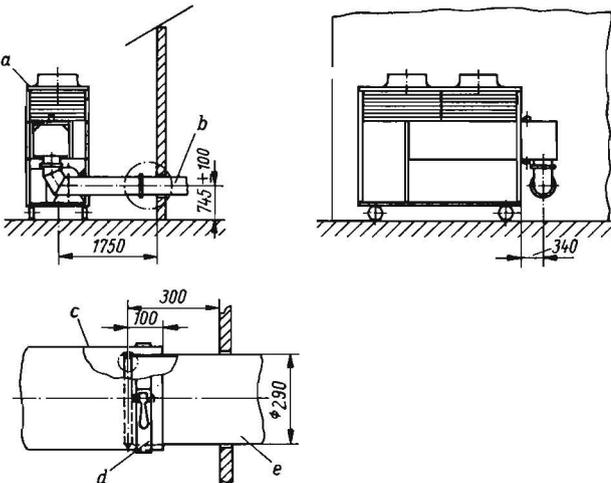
Anschluß des Getreidekühlers an ein Silo: a Maliplastik-Rohr, b Schlauchverschluß, c Stahlrohr (bauseitig), d Luftführungsröhre (Ausführung der dachförmigen Luftführungsröhre nach Angaben der zentralen Untersuchungsstelle für Getreidelagerung und Getreideumschlag Magdeburg/Frohse), e Getreidekühler
